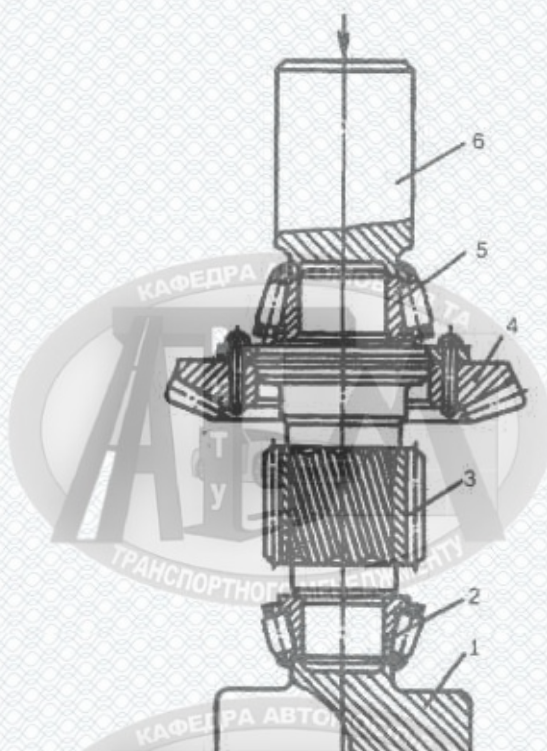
Перевірка затягування підшипників валу ведучої конічної шестерні [11]
